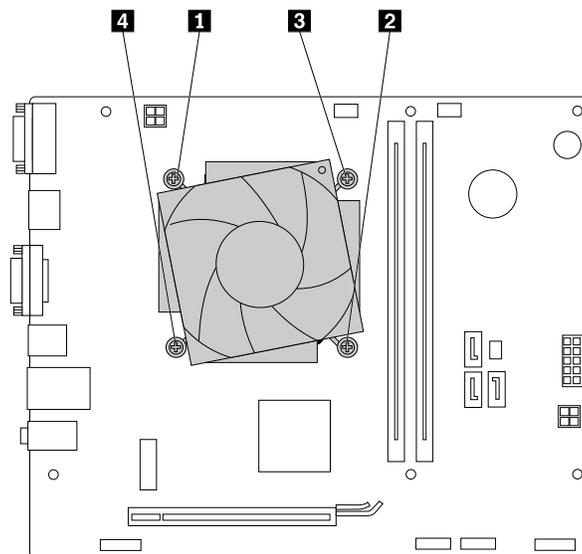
Extracción del conjunto de ventilador y disipador de calor
